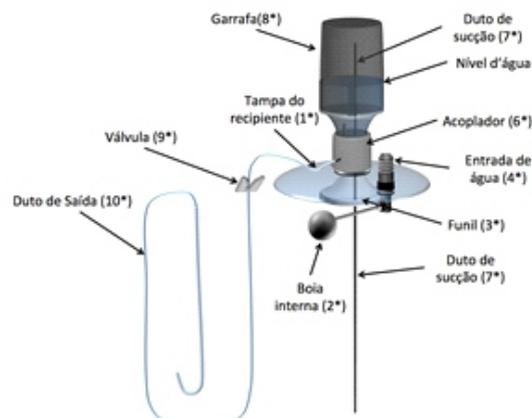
Instalação do acoplador (6*) e da garrafa preta (8*) sobre a tampa da bombona.
